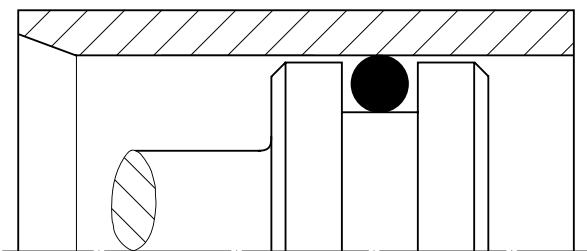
Nut im Innenteil („Kolbendichtung“): O-Ring radial verpresst
